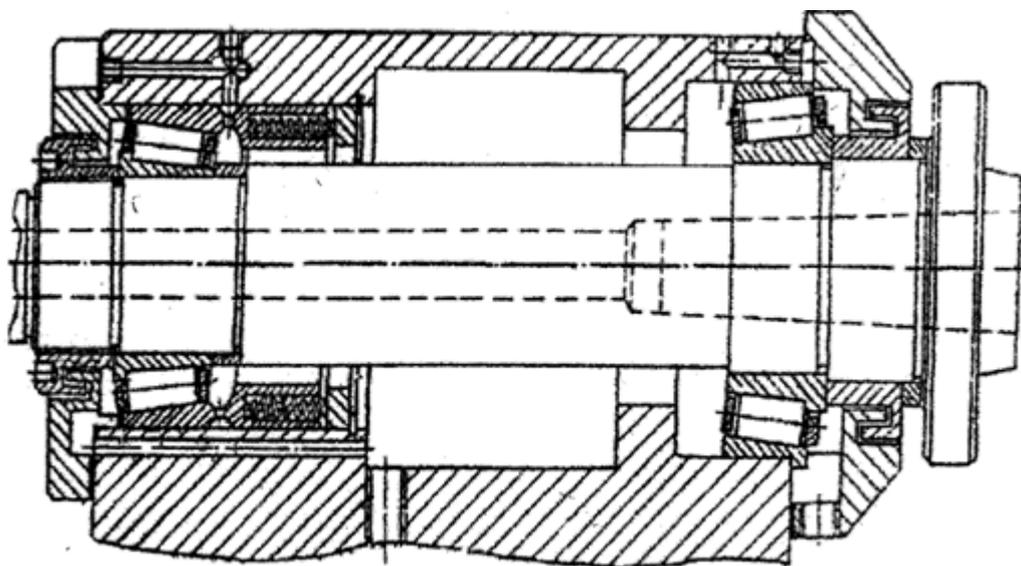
Шпиндельный узел станка с ЧПУ на роликоподшипниках с упорным бортом типа 67000 в передней опоре и типа 17000 в задней опоре
